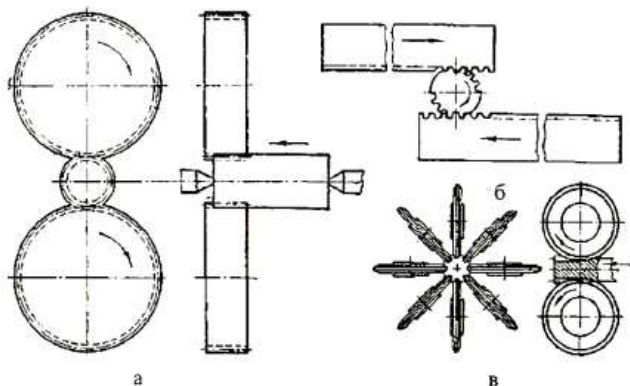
Принципова схема накручування шліців: а – круглими роликми; б – рейками; в – багатороликовою головкою
